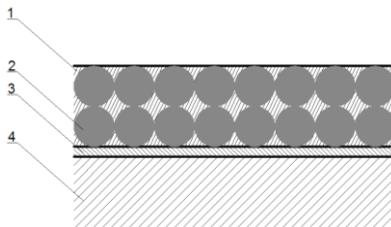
Схема металлофторопластового ленточного материала:
